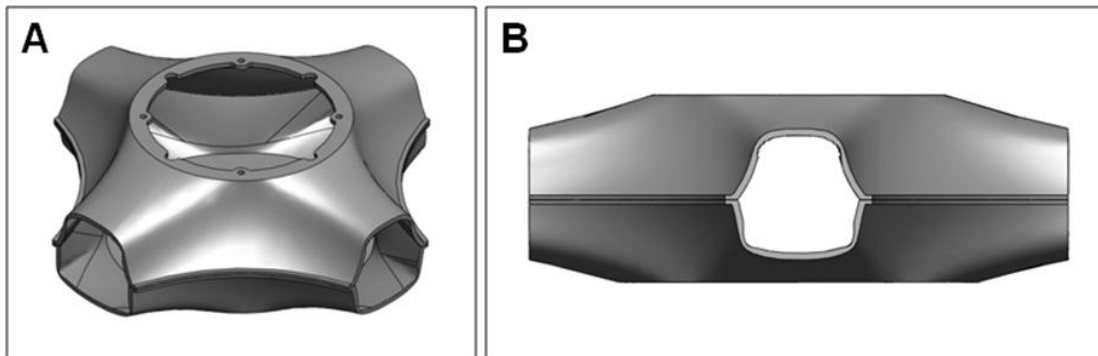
Diseño detallado de las secciones superior e inferior del fuselaje
